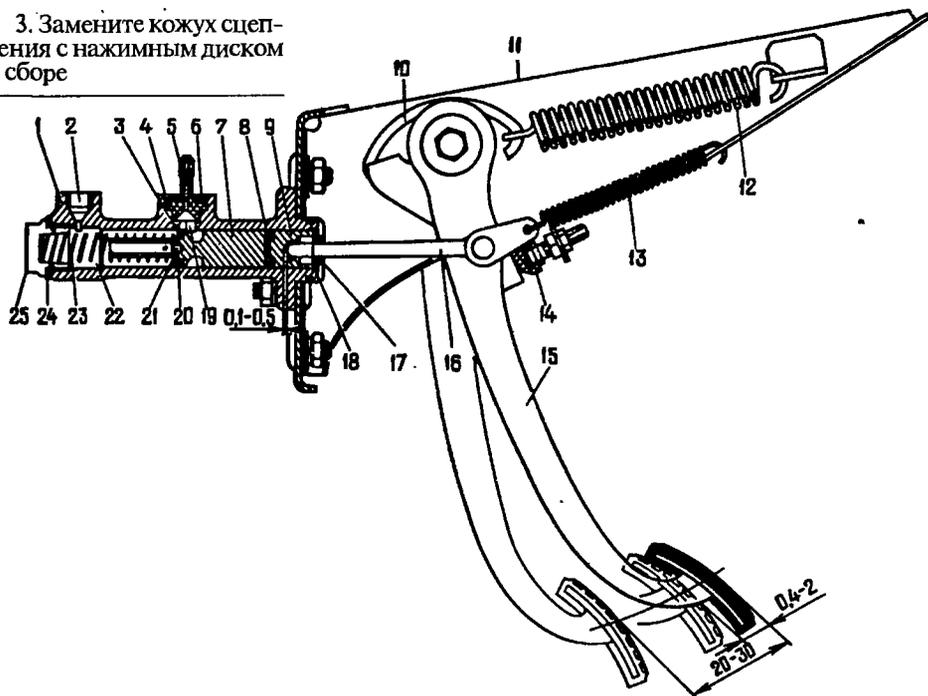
Педаль и главный цилиндр привода сцепления: 1 - корпус главного цилиндра; 2 - гнездо; 3 - перепускное (компенсационное) отверстие; 4 - прокладка штуцера; 5 - штуцер; 6 - стопорная пружинная шайба; 7 - поршень главного цилиндра; 8 - уплотнительное кольцо; 9 - поршень толкателя; 10 - крючок; 11 - кронштейн педалей сцепления и тормоза; 12 - пружина сервопривода педали сцепления; 13 - оттяжная пружина педали сцепления; 14 - ограничитель хода педали сцепления; 15 - педаль сцепления; 16 - толкатель поршня; 17 - защитный колпачок; 18 - стопорное кольцо; 19 - впускное отверстие; 20 - уплотнительное кольцо (кольцевой клапан); 21 - перепускное отверстие поршня; 22 - рабочая полость цилиндра; 23 - пружина; 24 - прокладка; 25 - пробка
